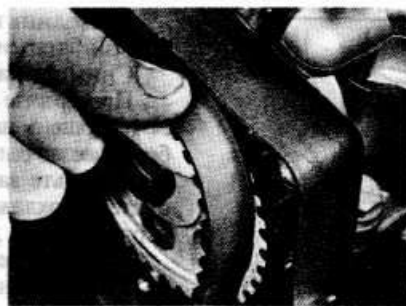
Снятие ремня с звездочки — двигатель 1,6 л
